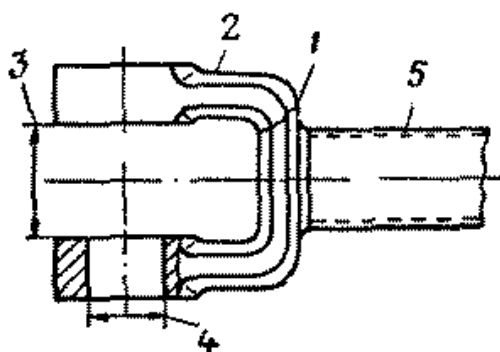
Опорная вилка оттяжного рычага нажимного диска сцепления
